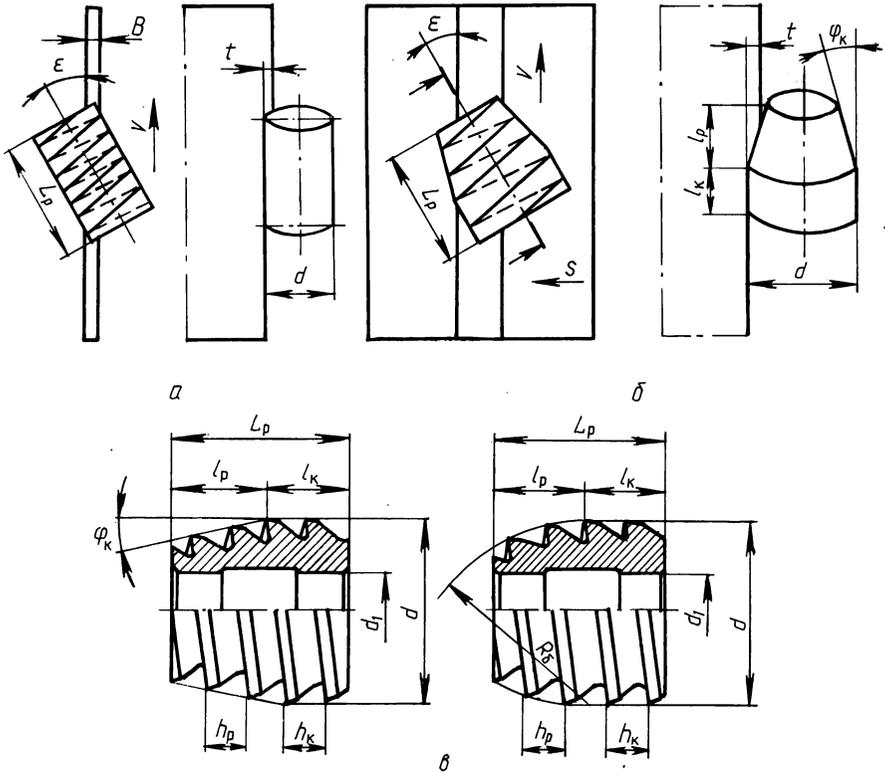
Схемы обработки винтовыми ротационными резцами плоских поверхностей и конструкции режущих частей для них
